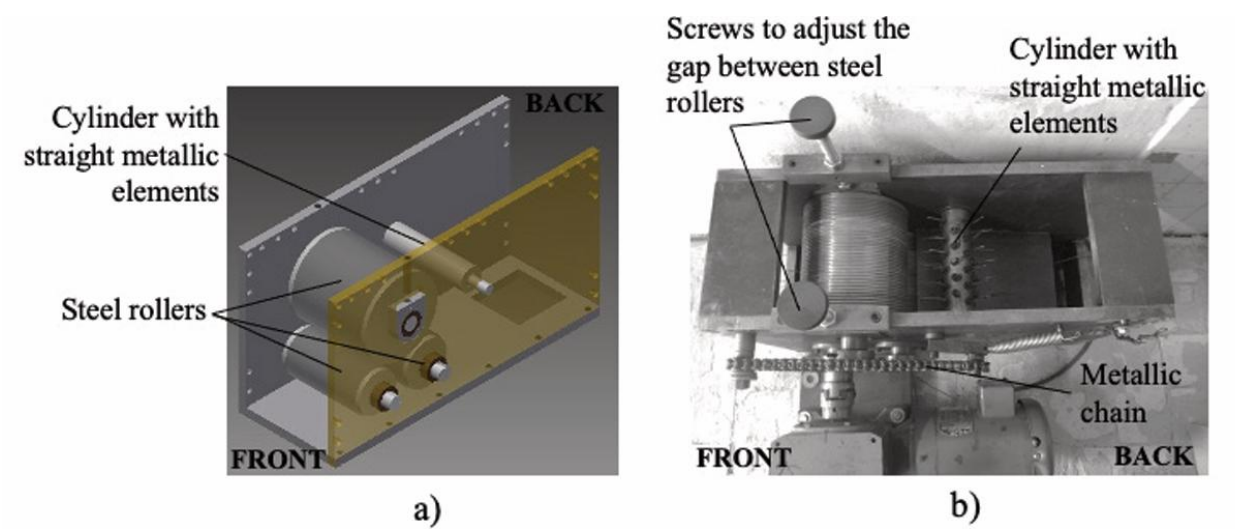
Método combinado químico – mecánico Rollet mil Crushing Machine + Crushing.
